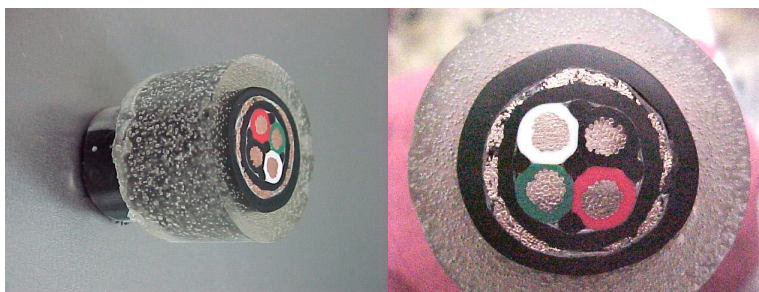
Parte do cabo embutida em resina para análise dimensional
